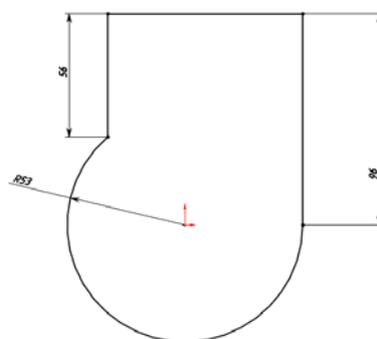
Эскиз для второго и третьего способов получения заготовки корпуса
